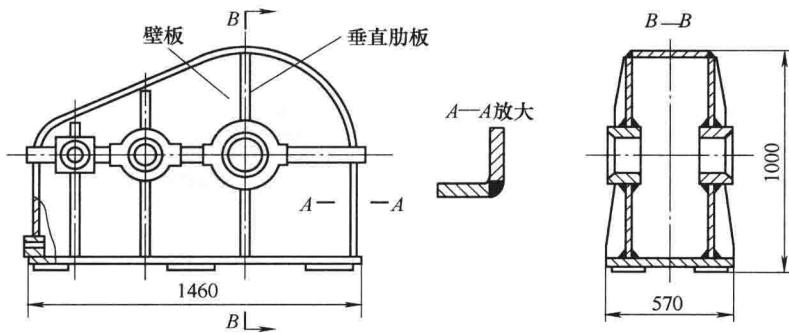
单壁剖分式减速器箱体焊接结构
